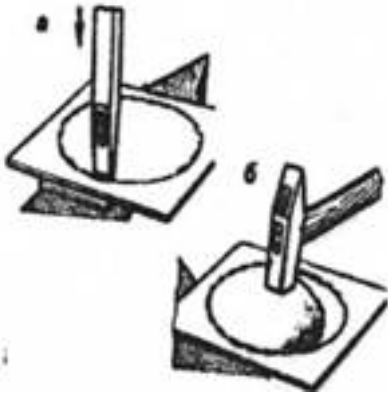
Вирубівання заготовок з листового металу:
